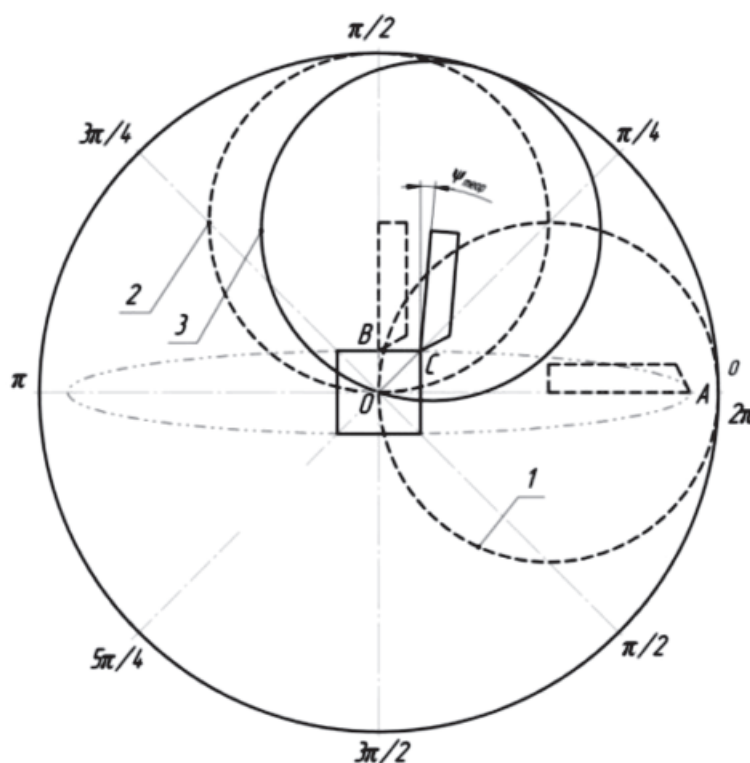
Схема перемещения вершины режущей кромки инструмента в процессе обработки:  $\psi_{\text{теор}}$  – величина изменения кинематического переднего угла инструмента;  $O$  – центральная точка; 1 – положение резцового блока в точке начала перемещения режущего инструмента;  $A$  – точка начала перемещения вершины режущей кромки; 2 – положение резцового блока в точке, в которой кинематические углы равны геометрическим;  $B$  – точка вершины режущего инструмента, в которой кинематические углы равны геометрическим; 3 – положение резцового блока в момент врезания;  $C$  – точка вершины инструмента в момент врезания
